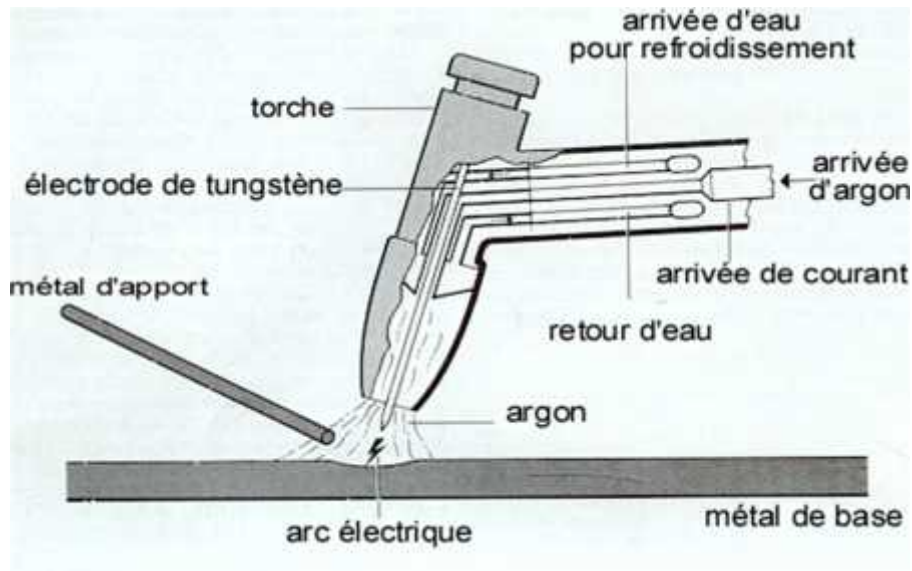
Soudage TIG / Soudage sous argon
